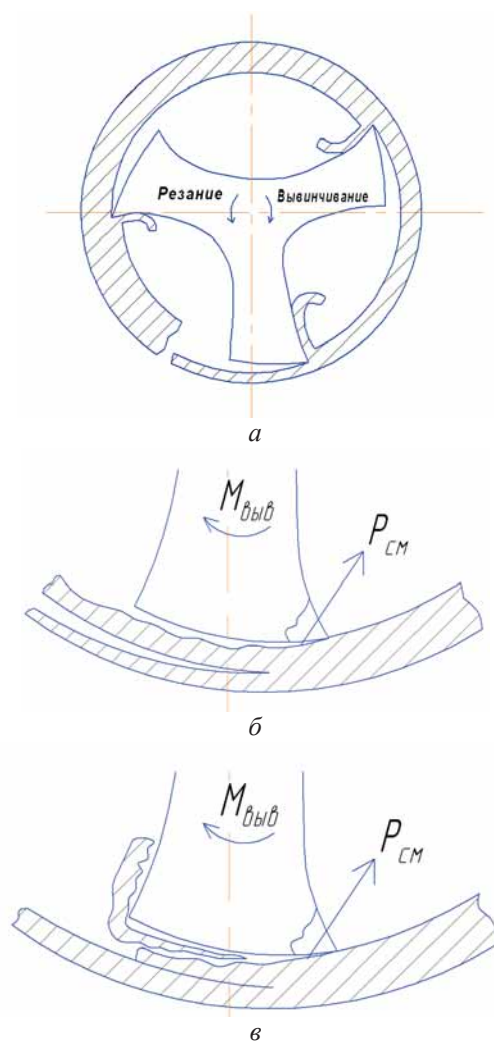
Схема нарезания резьбы метчиком: а – схема отделения стружки режущими зубьями метчика; б – взаимодействие зуба метчика с обрабатываемой поверхностью при его повороте на один угловой шаг зубьев; в – схема заклинивания зуба оторвавшимся элементом стружки
